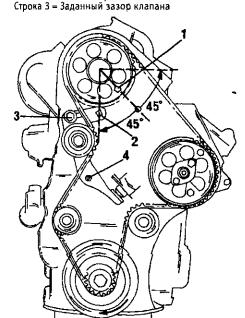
Положение зубчатого шкива при снятии распределительного вала.
